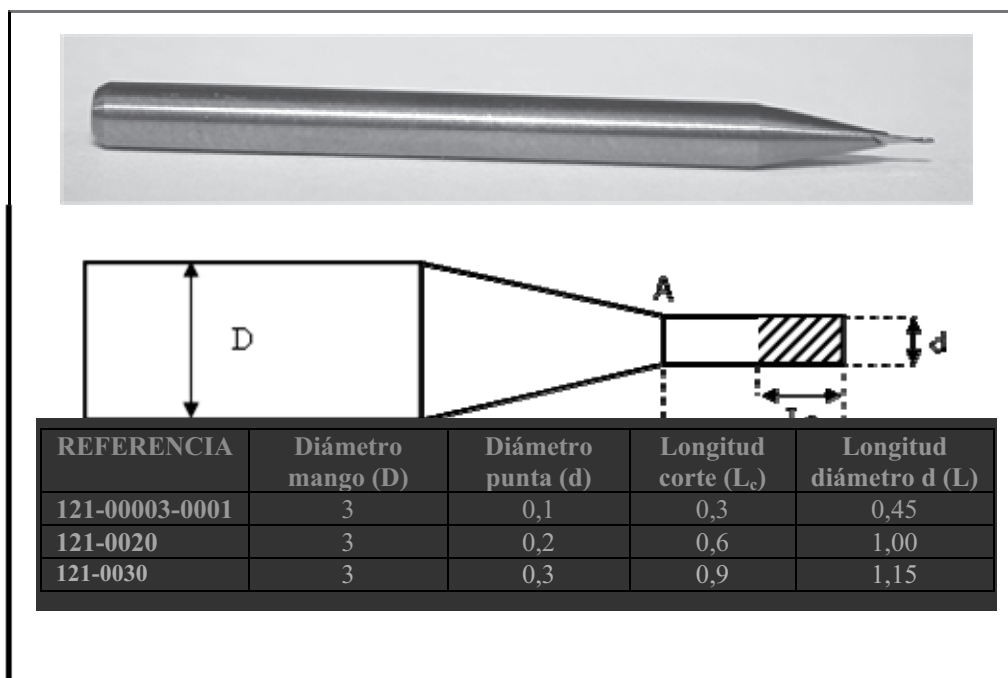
Fresas frontales empleadas (dimensiones en mm).
